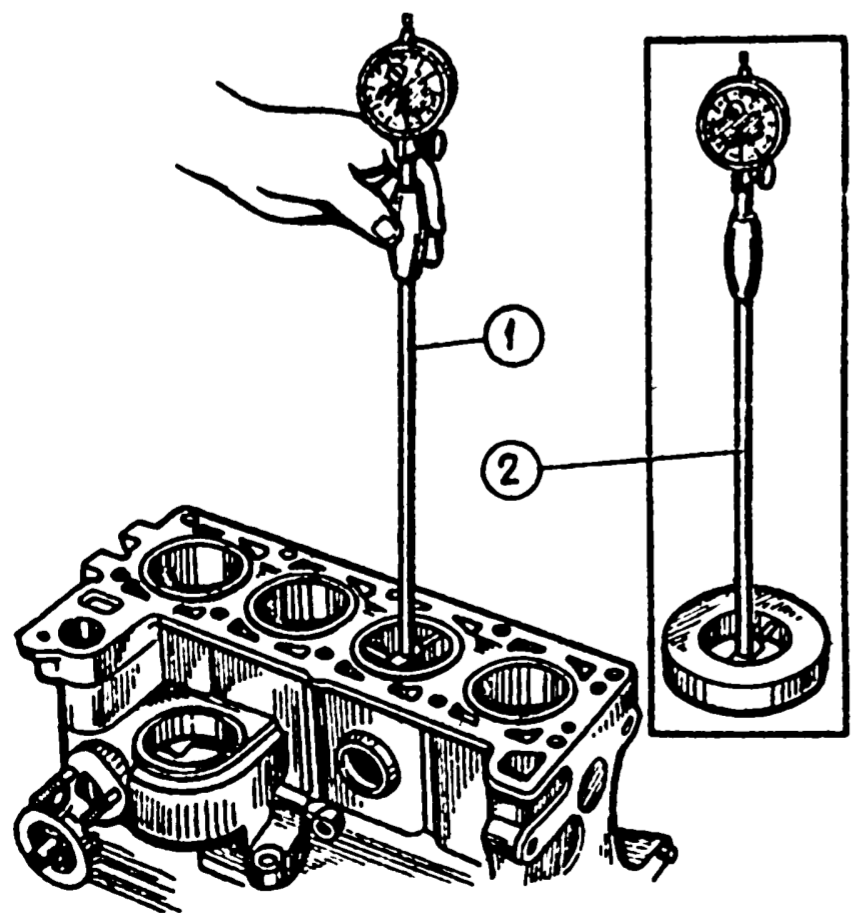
Измерение цилиндров нутромером: 1 - нутромер; 2 - установка нутромера на ноль по калибру
